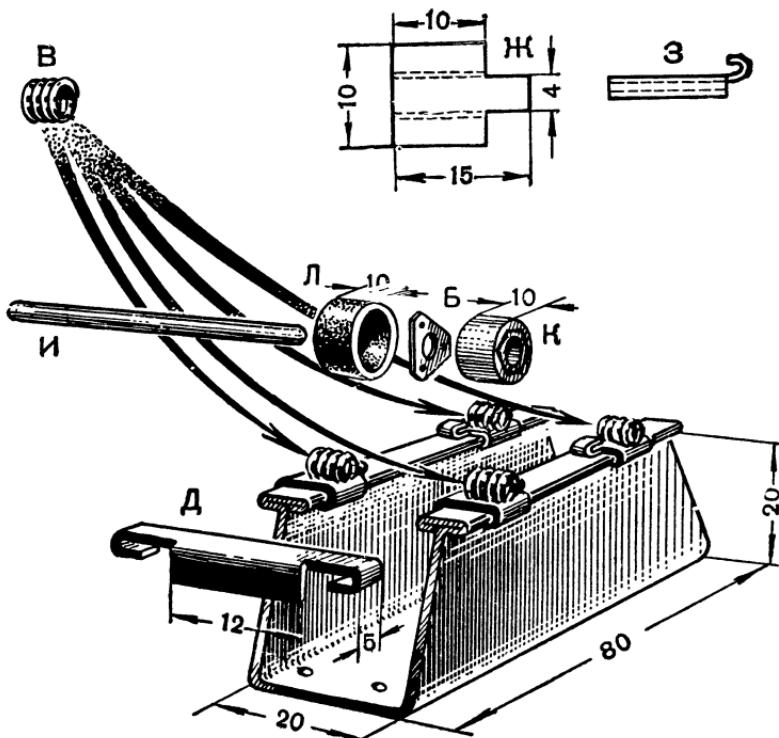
Детали и порядок сборки редуктора № 3 (рис. 111):
